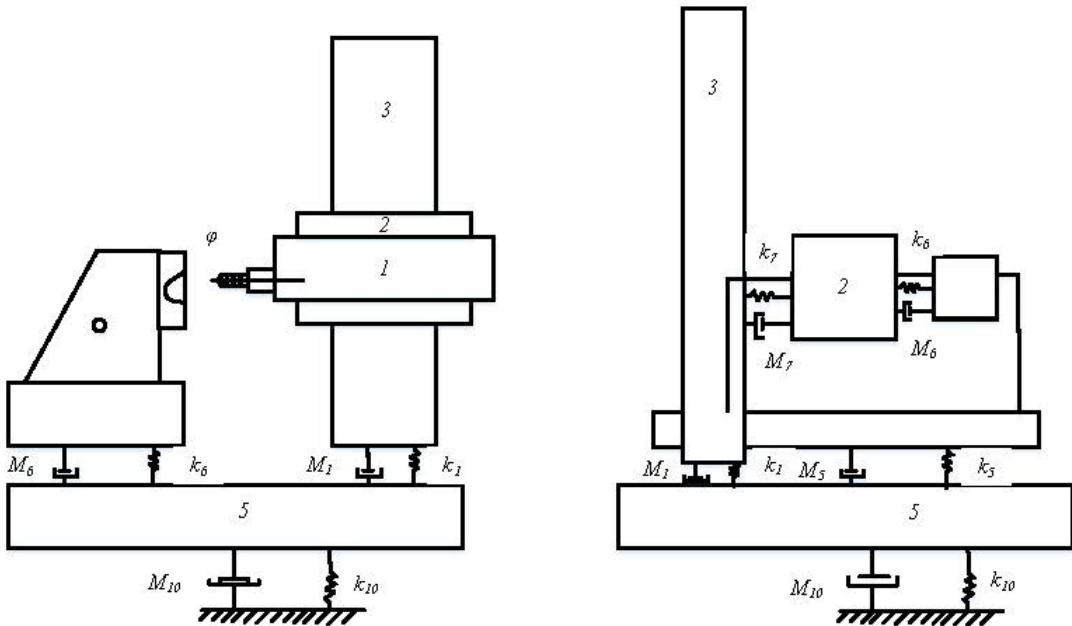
Розрахункова схема дискримінанту динамічної моделі фрезерного верстата
